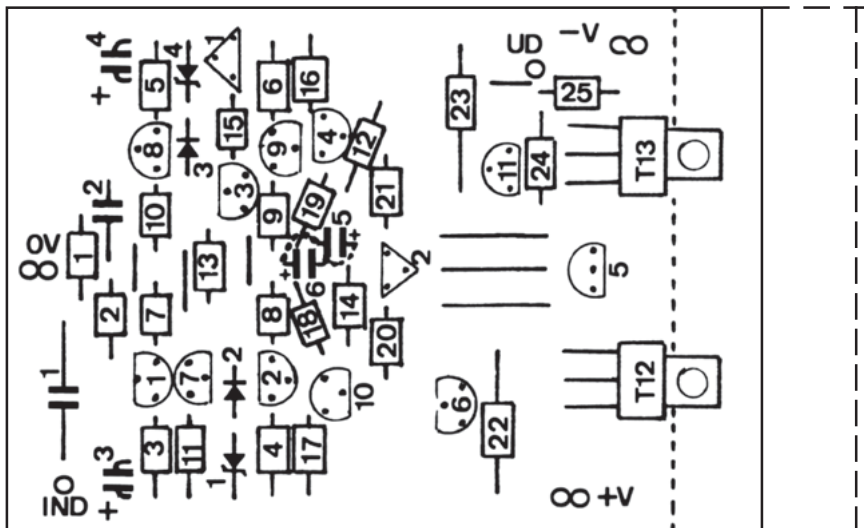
Komponent-layout for en kanal af forstærkeren set fra komponentsiden. Hullerne til transistorskruerne bores med et 3,2 mm bor.
